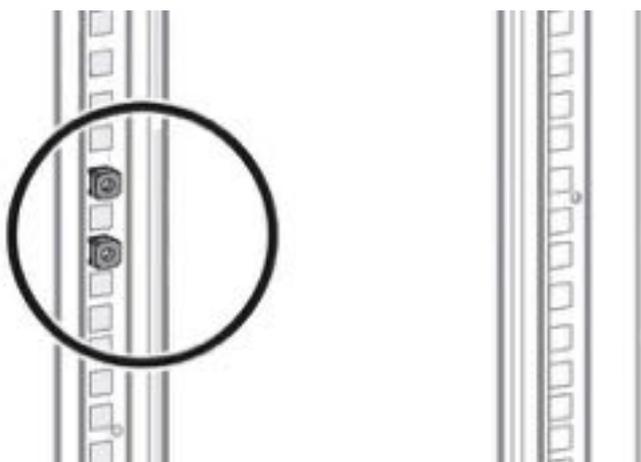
Установка клетевых стоечных гаек в монтажной стойке.
